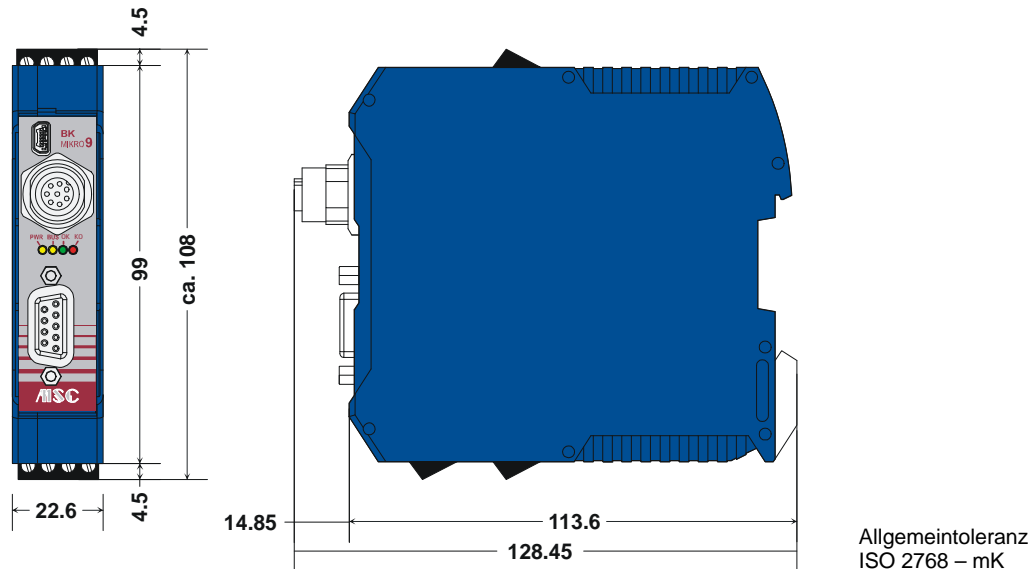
Mechanische Abmessungen – Steuergerät BK MIKRO9
